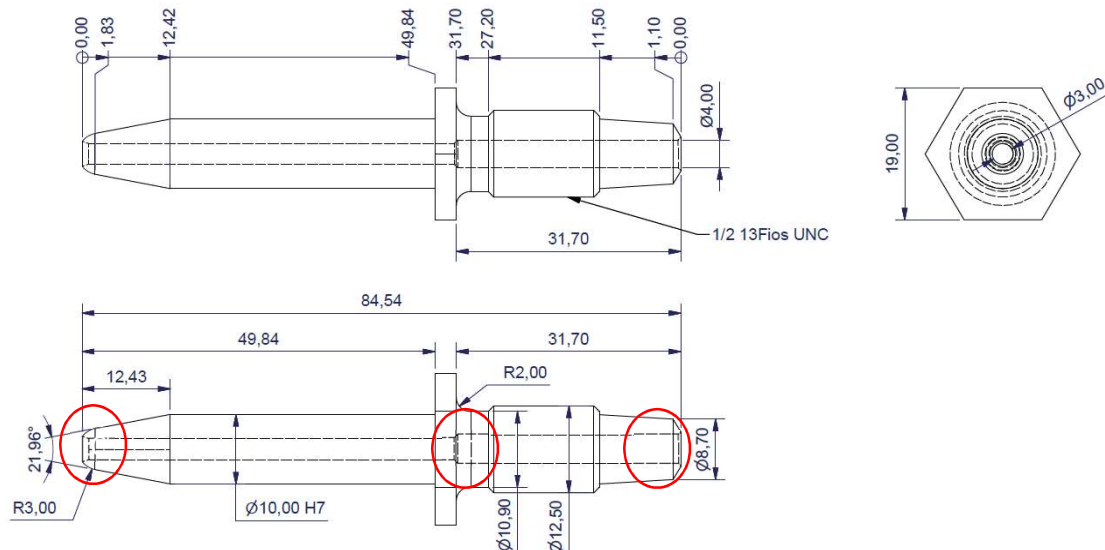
Geometria e dimensões do bico de injeção utilizado
